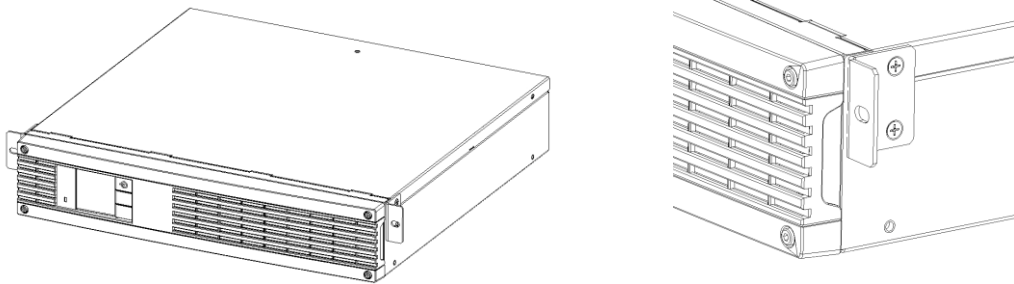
Montaż zestawu szyn (Rack Kit)
